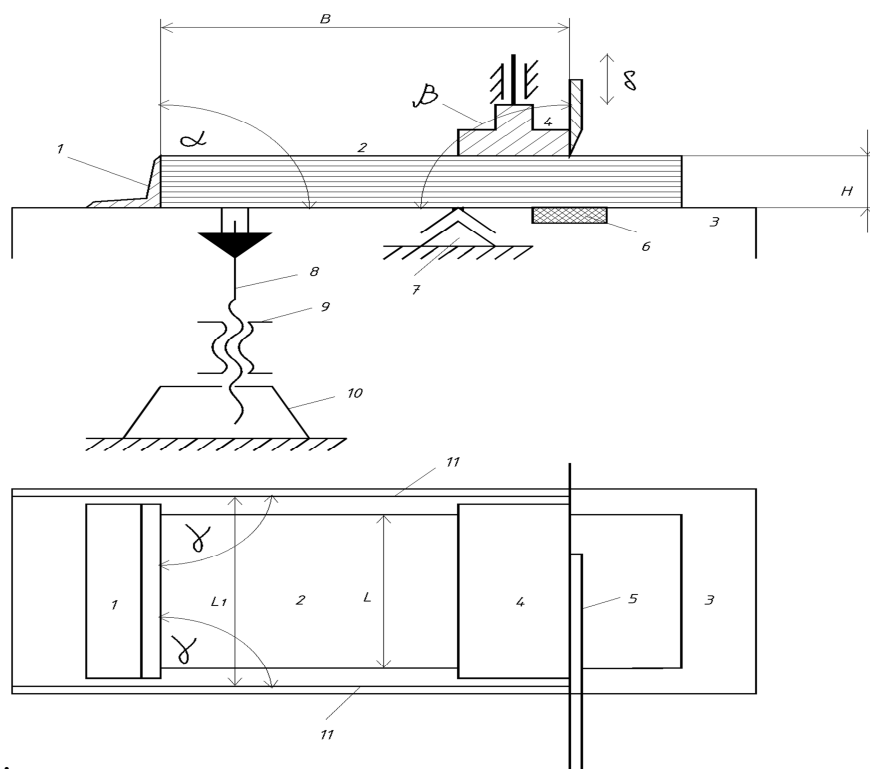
Технологічна схема машини для різання паперових заготовок з одним ножом: 1 - подавач; 2 - банк заготовок; 3 - робочий стіл; 4 - прижим; 5 - ніж; 6 - опора ножа; 7 - призма; 8 - гвинт; 9 - гайка; 10 - супротивна опора; 11 - планка бокова
